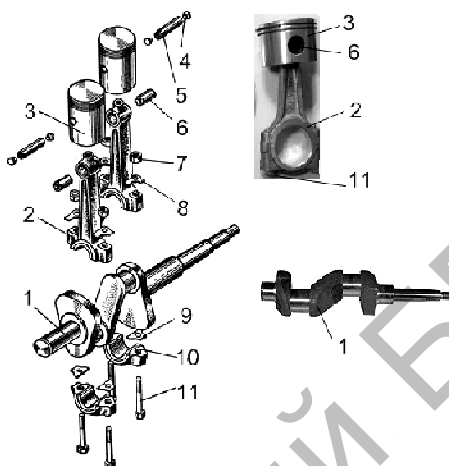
Кривошипно-шатунный механизм компрессора:
